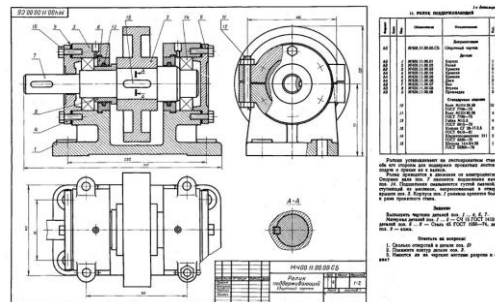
Сборочный чертеж «Ролик поддерживающий»
